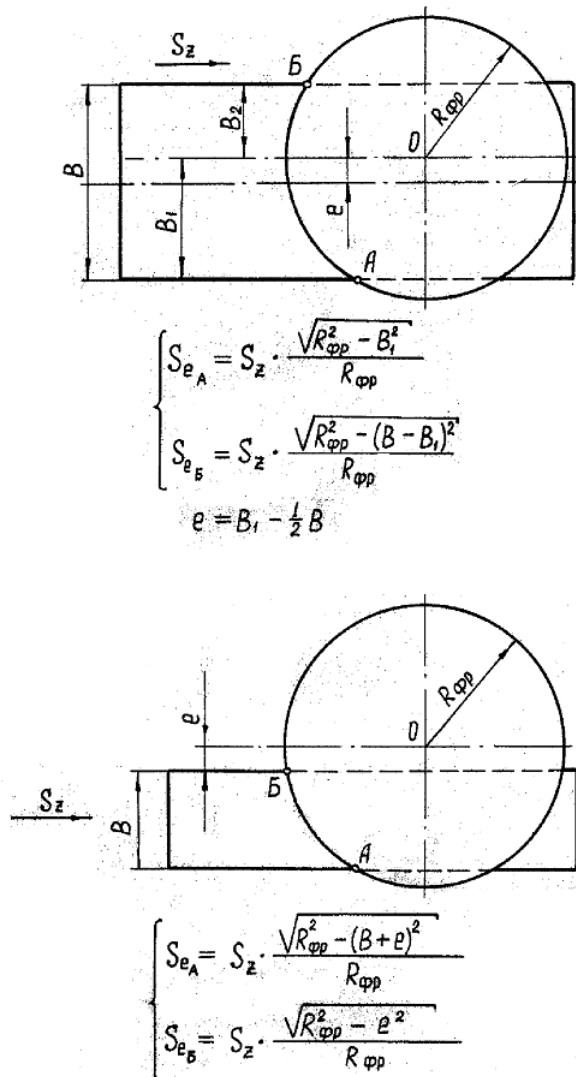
Зависимости для определения взаимного расположения фрезы и заготовки или их размеров
